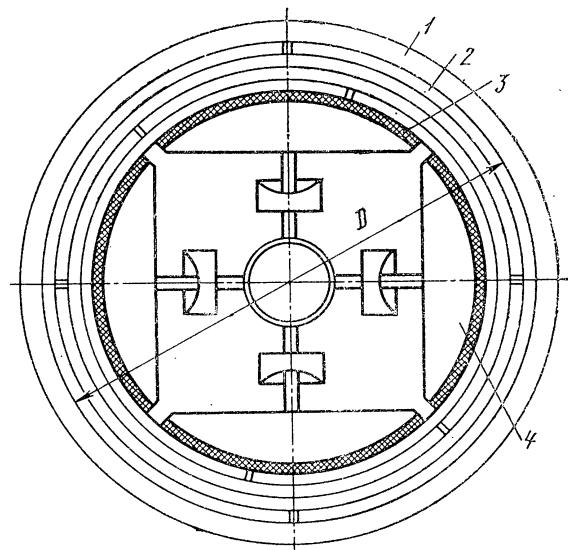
Схема склейивания заготовок замкнутого контура из планок в жесткой пресс-форме:
